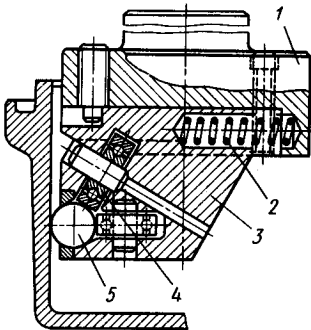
Шариковая копирующая раскатка для обработки отверстий в чугунном тормозном барабане: 1 — корпус; 2 — пружина; 3 — подвижная державка; 4 — опорный подшипник; 5 — шарик
